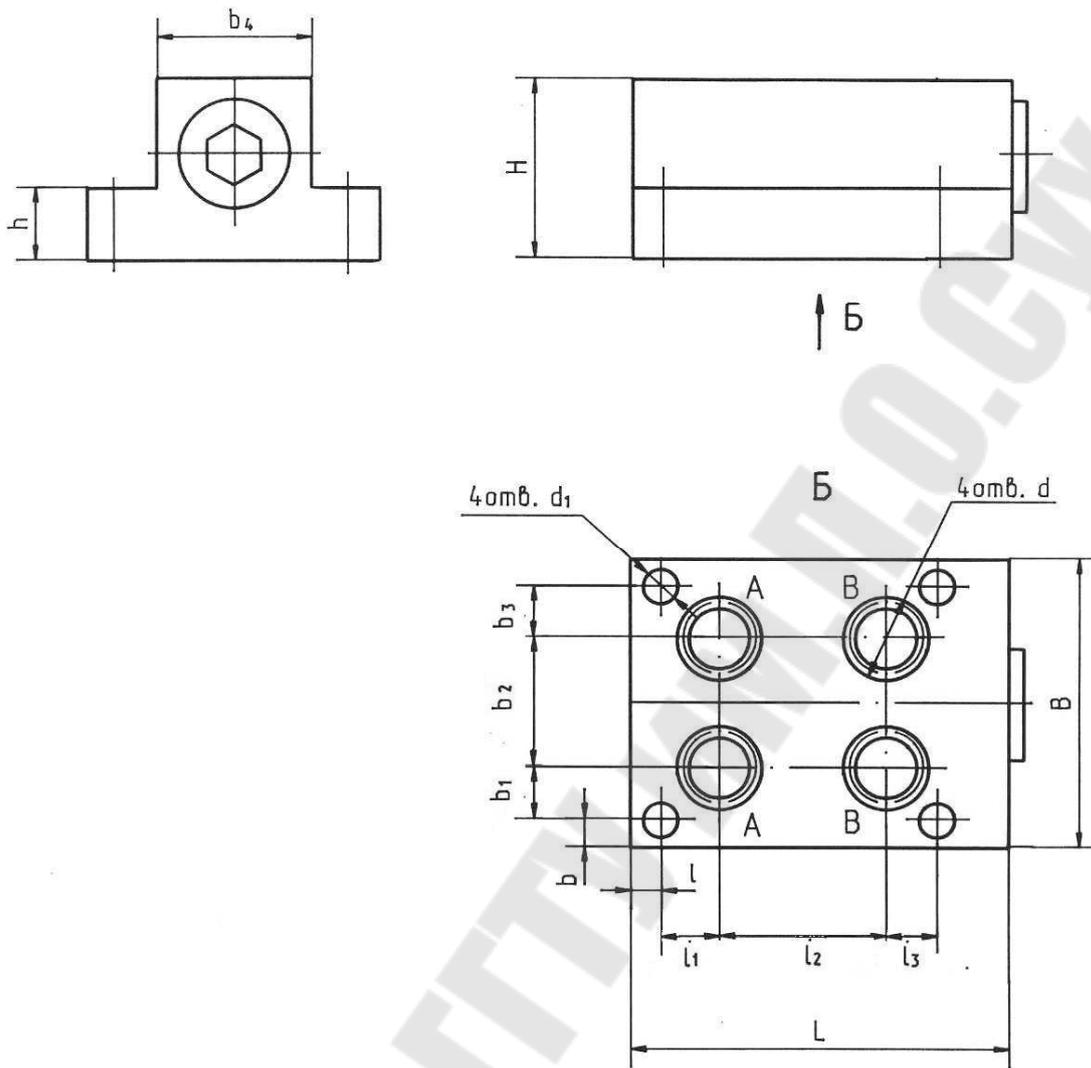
Общий вид блока присоединительного клапана обратного БПВ – 10 КО, БПВ – 16 КО, БПВ – 20 КО
